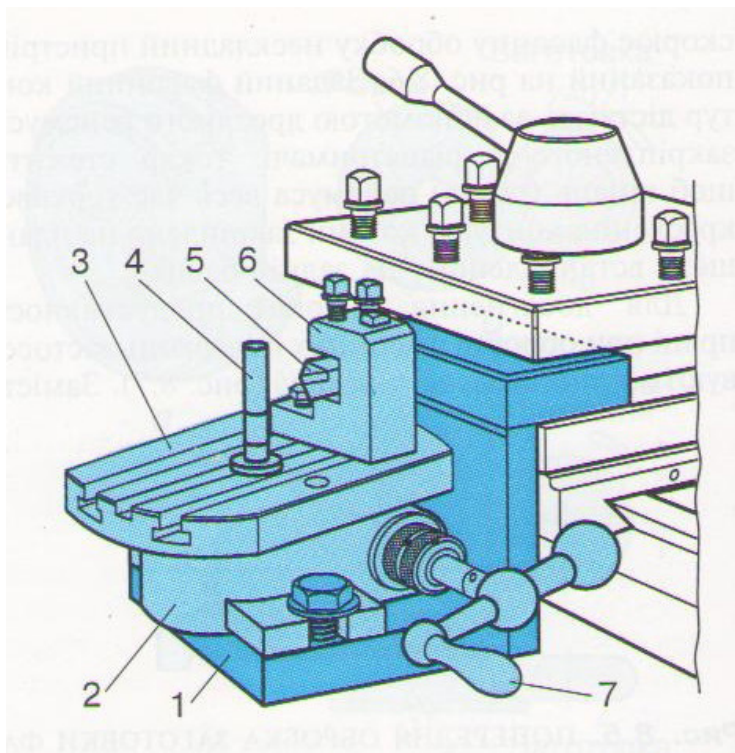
Пристрій з поворотним столиком для обробки сферичних поверхонь:
